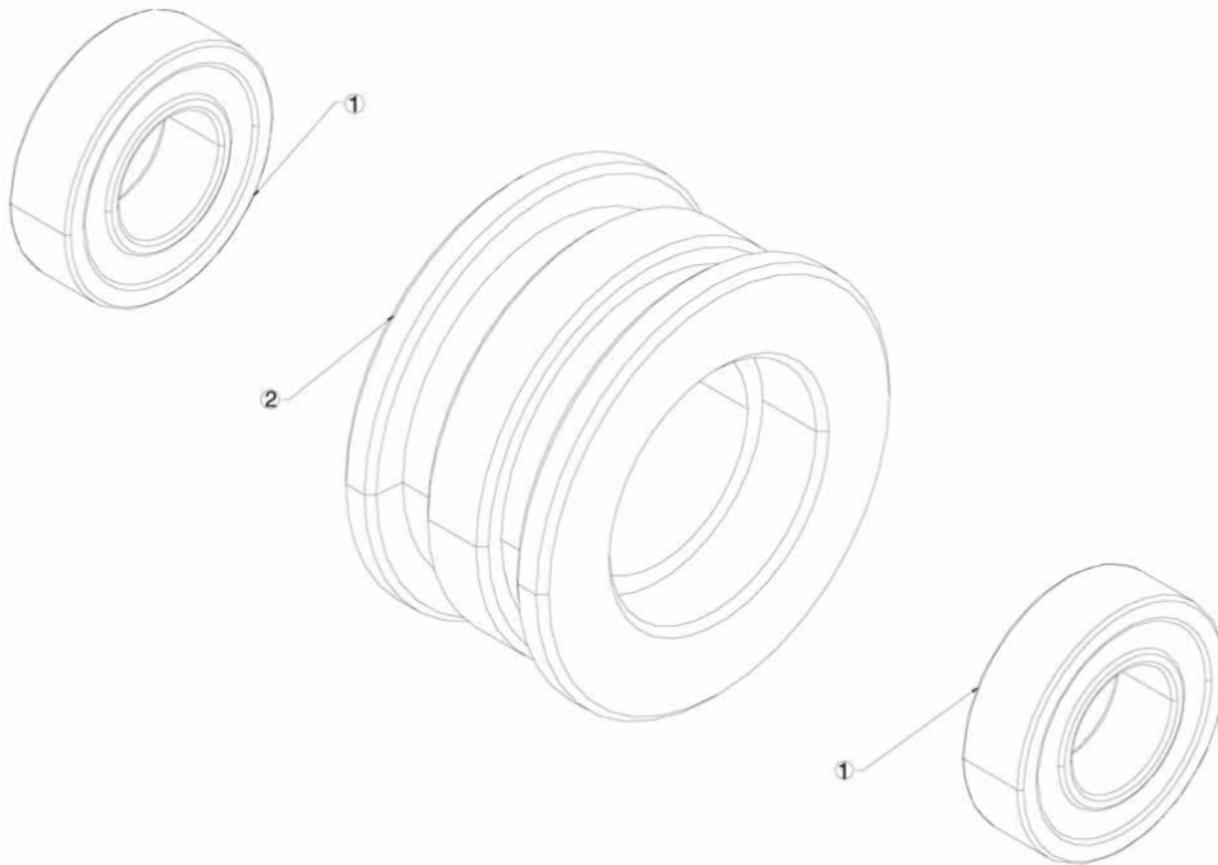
Чертеж сборки направляющего валика/цепи - A7008-00
